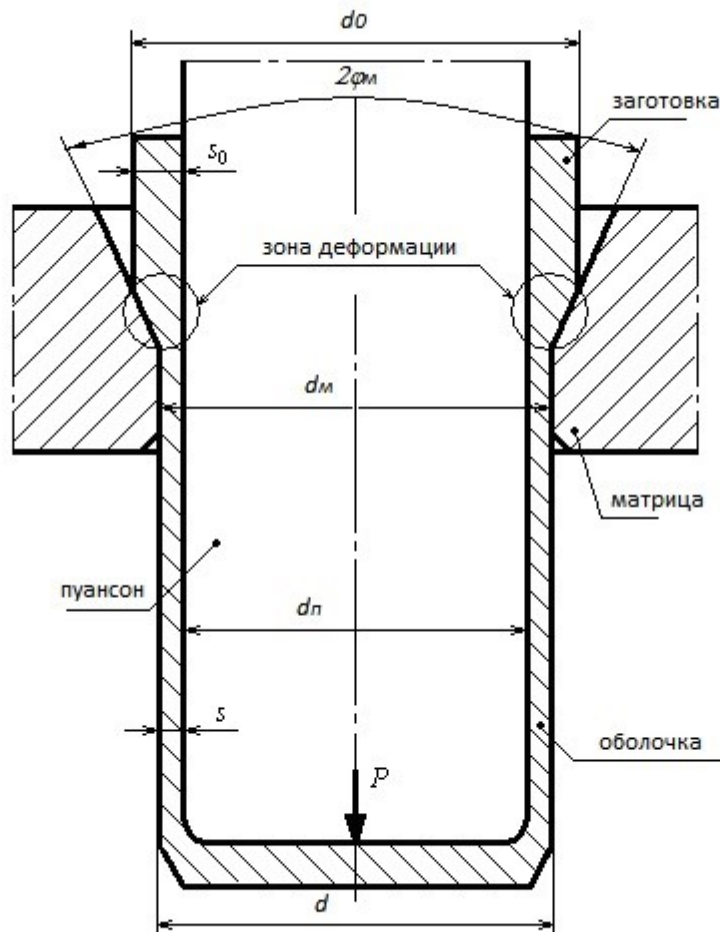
Схема процесса вытяжки цилиндрической оболочки
